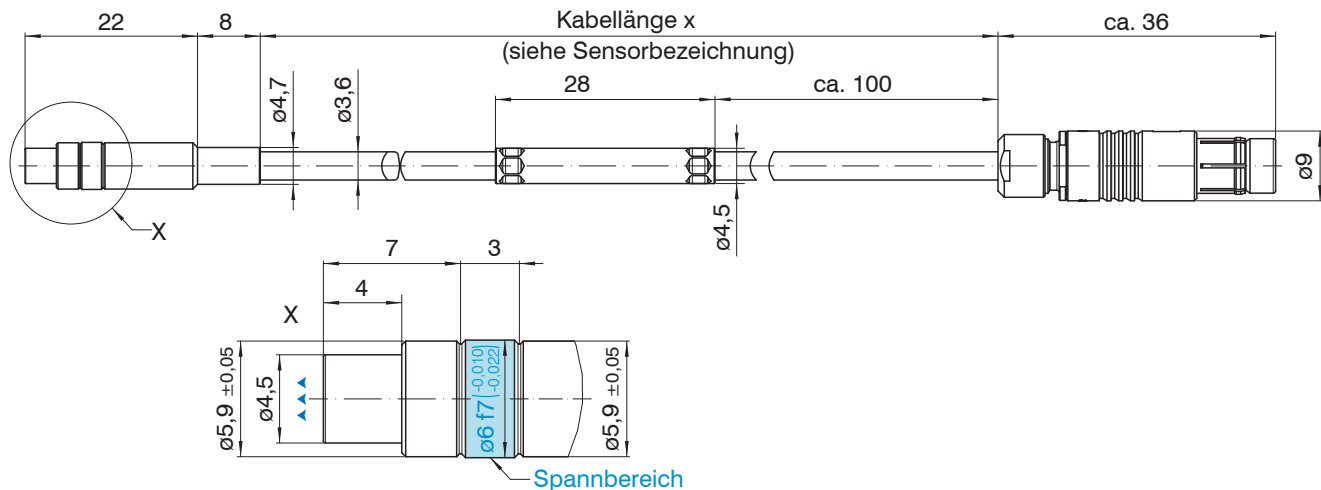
Maßzeichnung Sensoren ES-U1-T-CAx/mB0, Abmessung in mm
